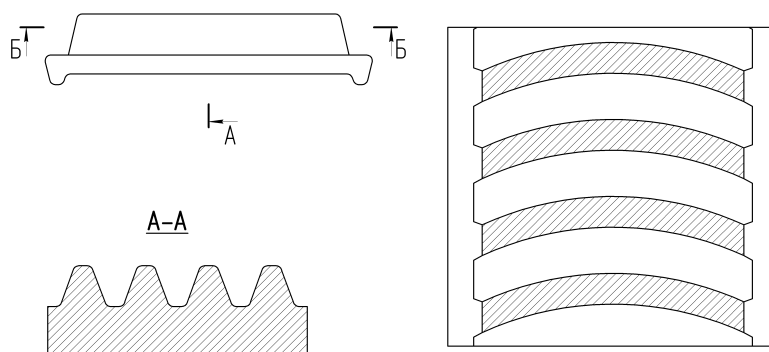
Зубчатая рейка с арочным зацеплением Новикова
